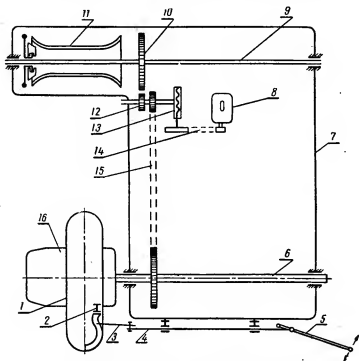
Схема специального станка для обрезки бортов и расслоения покрышки:
